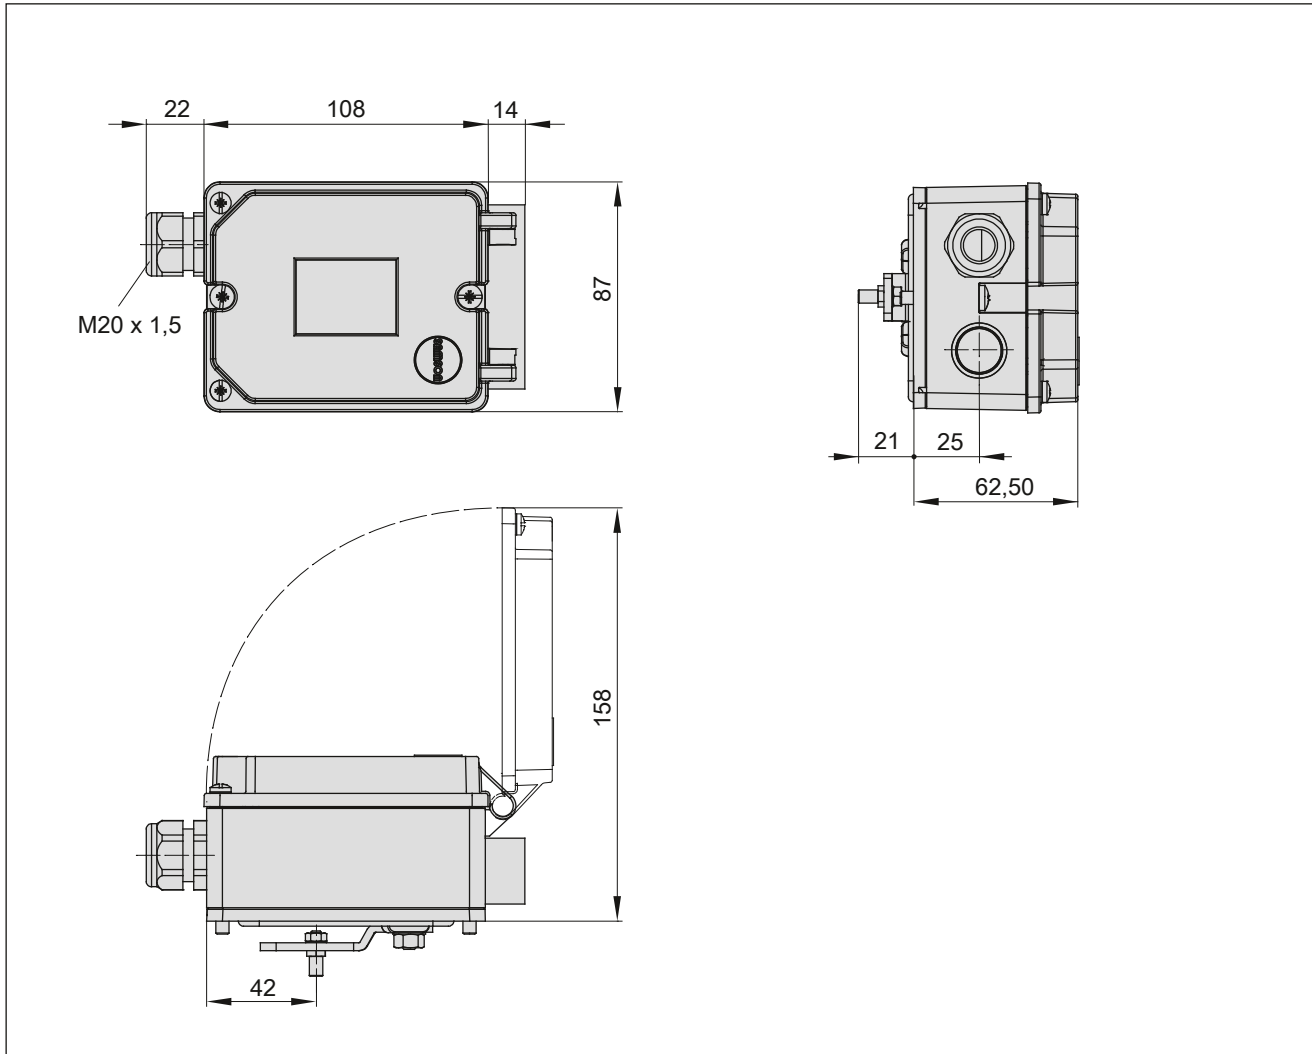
Dimensiones (mm) del posicionador electro neumático Tipo 3725 (versión del hardware GI:00)
